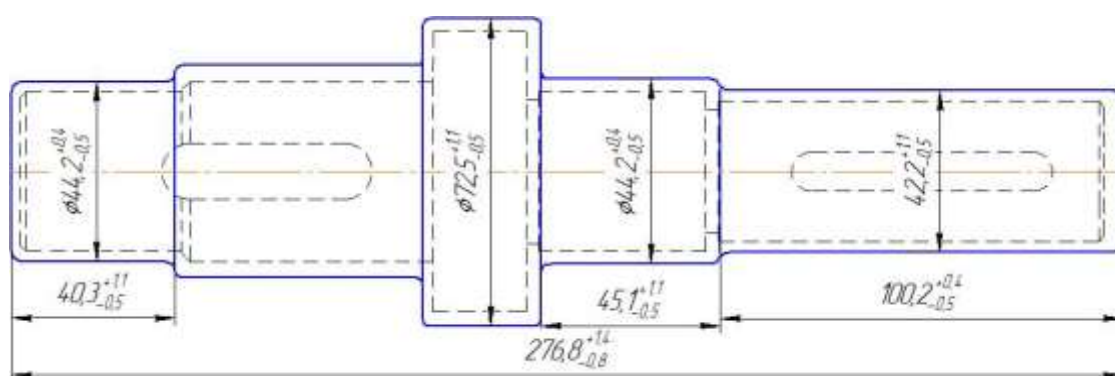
Заготовка отримана штампуванням на КГШП
